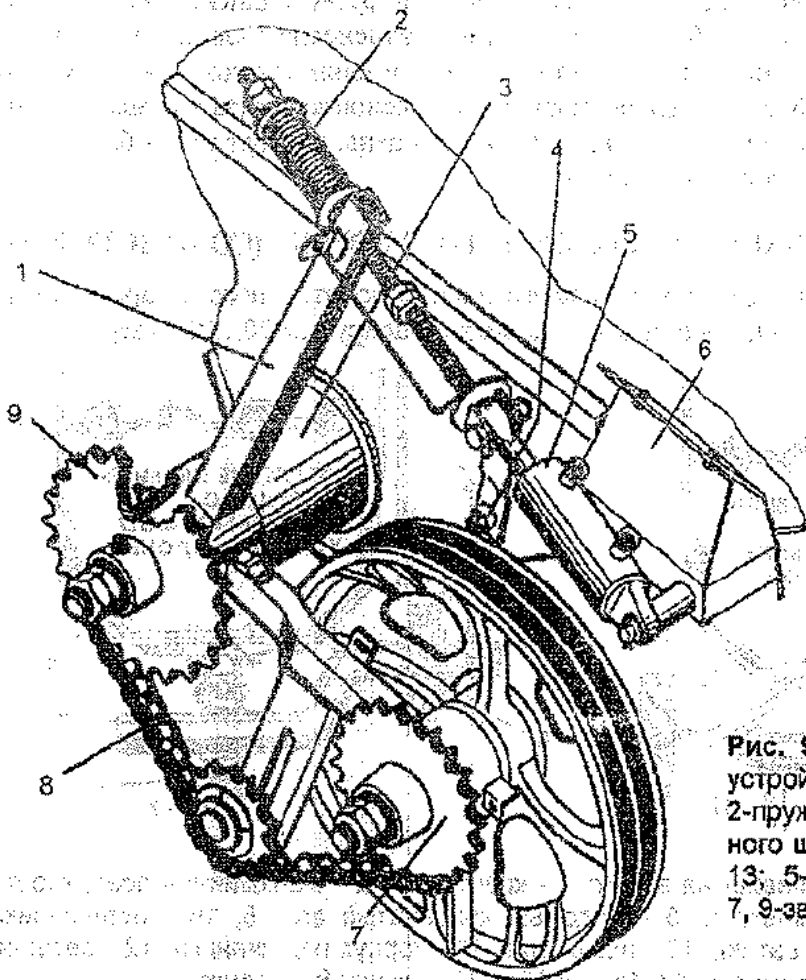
Контрпривод выгрузного устройства: 1-двулучевый рычаг; 2-пружина; 3-ступица горизонтального шнека бункера; 4-датчики ДО-13; 5-гидроцилиндр; 6-кронштейн; 7, 9-звездочка; 8-цепь
